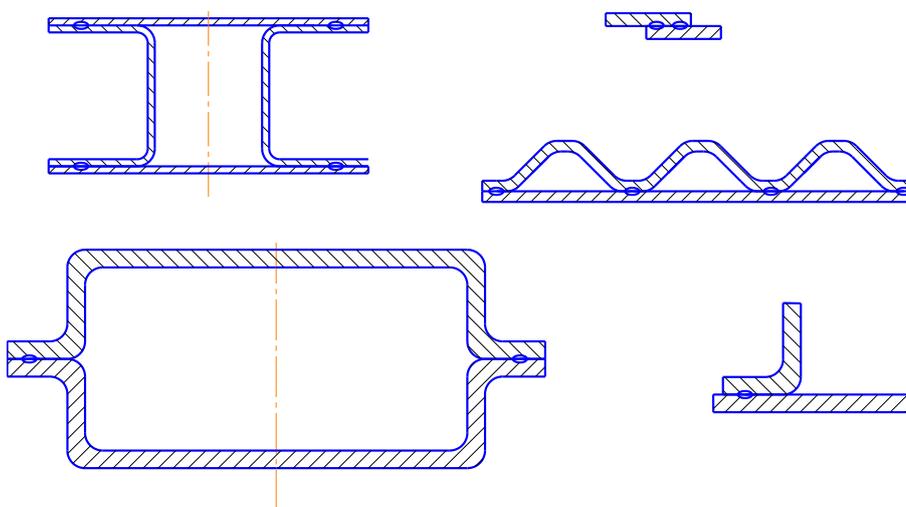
Примеры свариваемых деталей с помощью точечной сварки.
